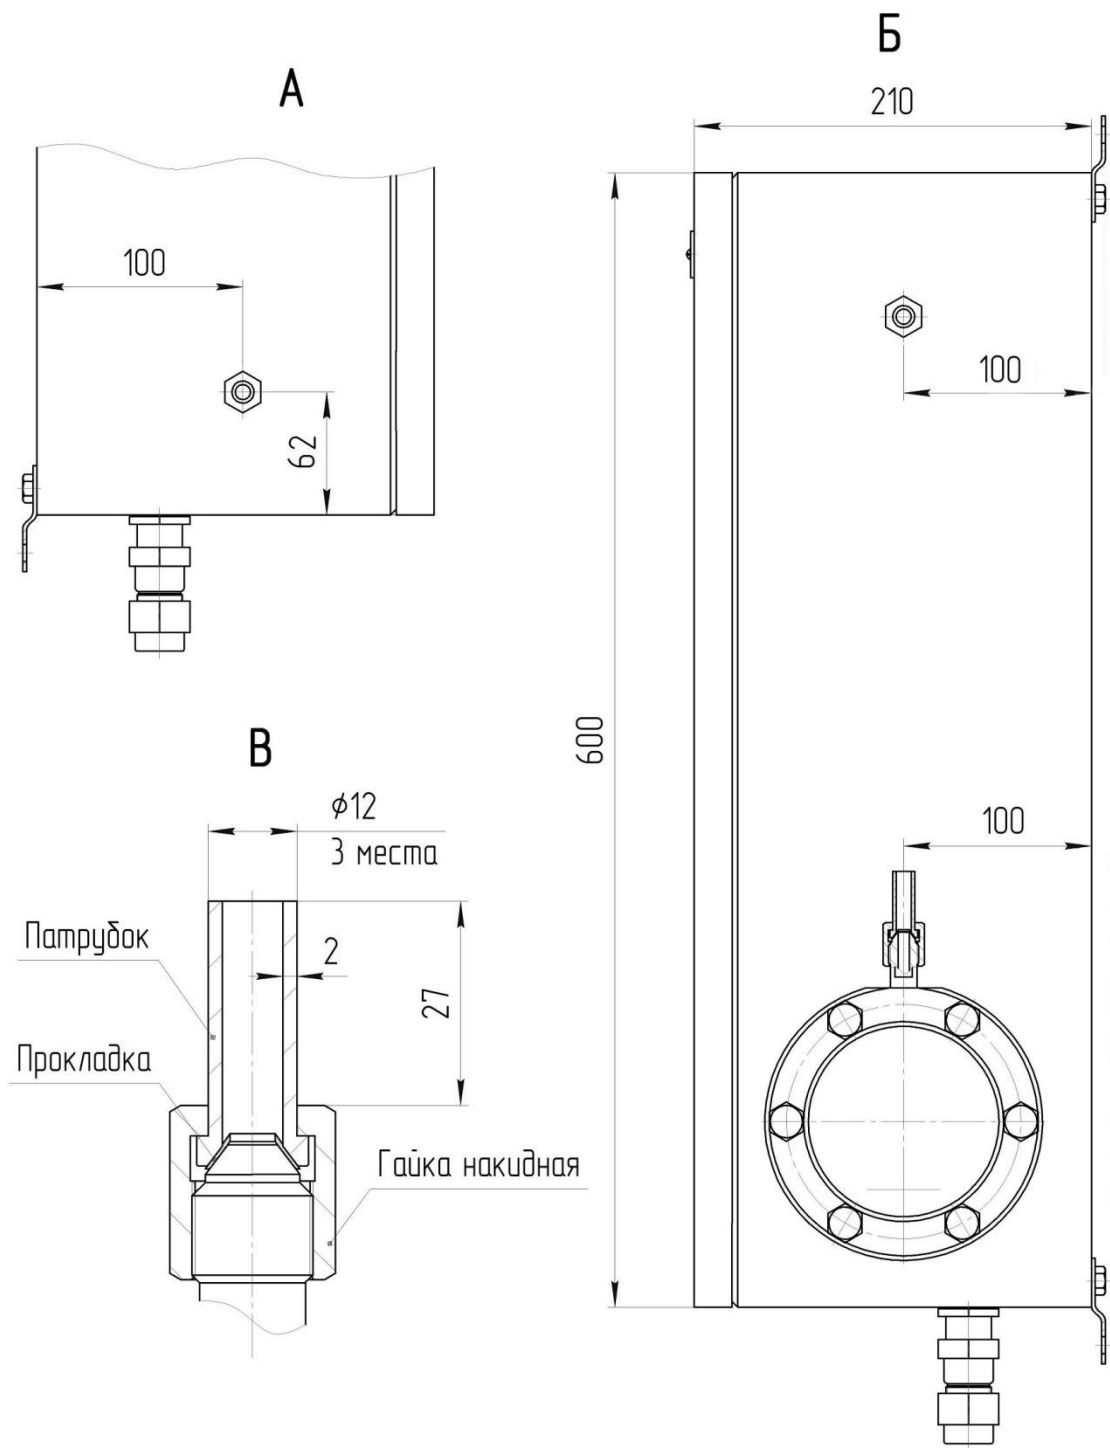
(лист 2 из 2) – Габаритные и присоединительные размеры дозатора
